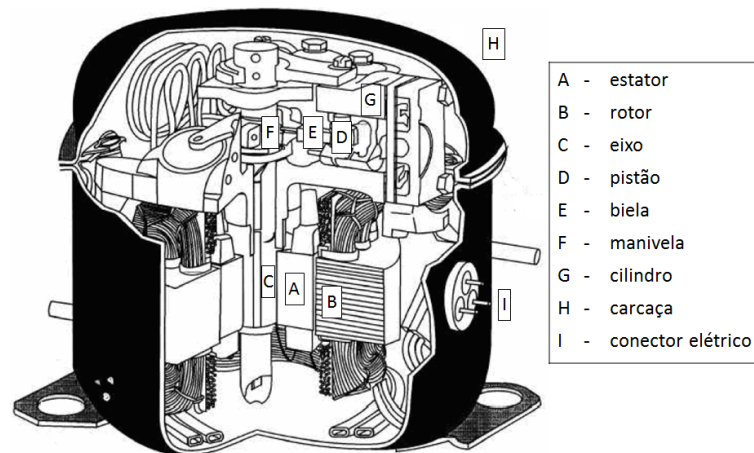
Compressor alternativo hermético. Adaptado de [2].
